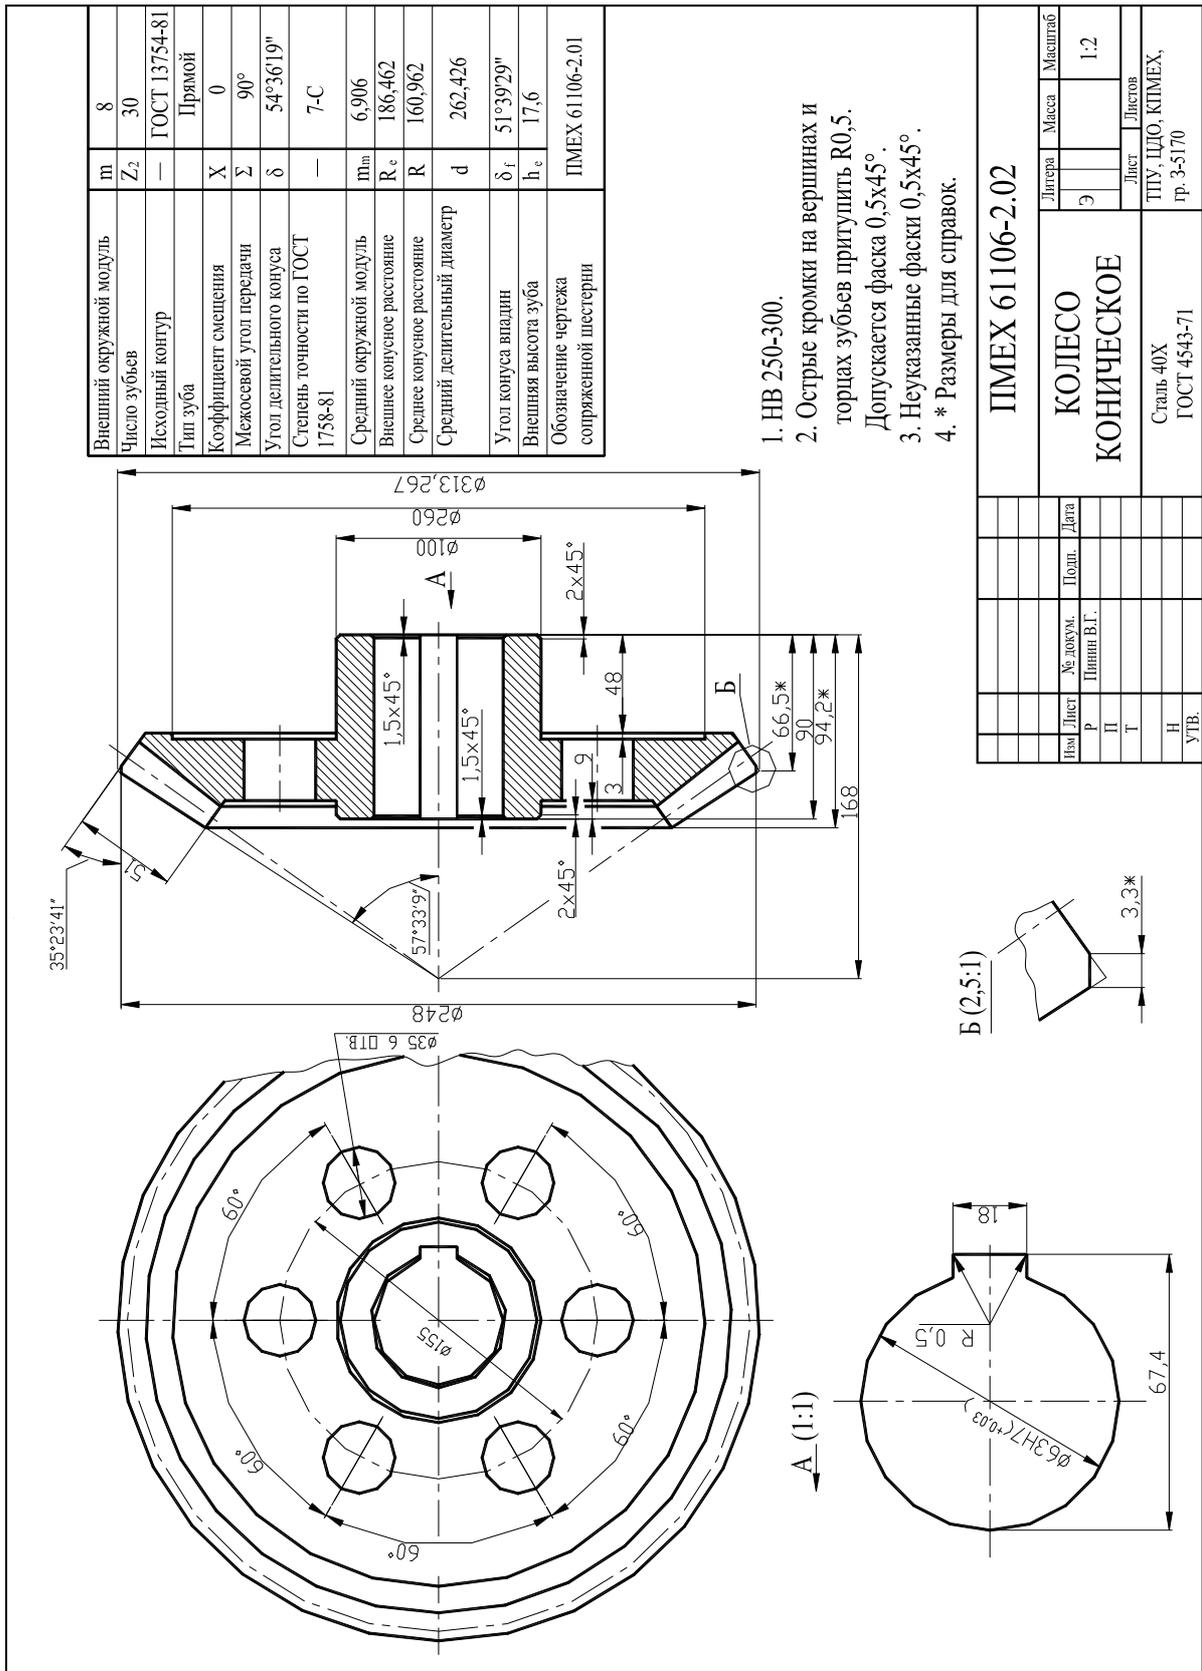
Пример выполнения эскизного чертежа эвольвентного конического зубчатого колеса
